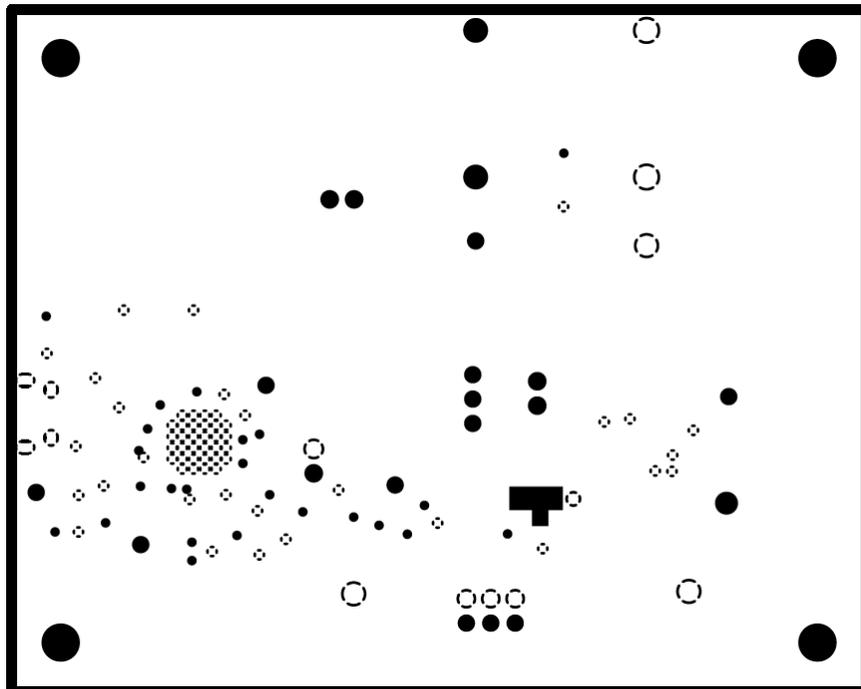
DAC121S101SEPEVM PCB 中层 1 布局 (接地平面)
